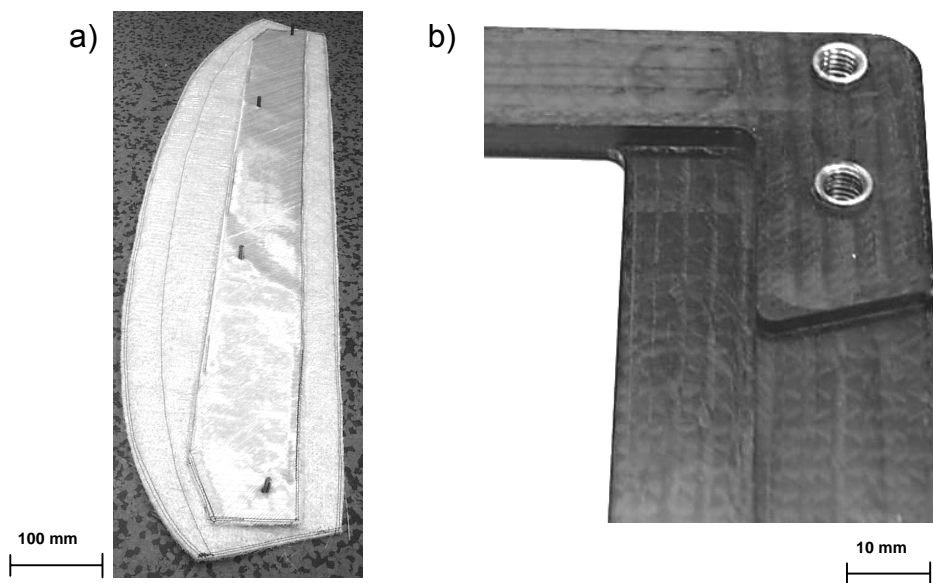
a) Spoilerlippenpreform für die Automobilindustrie, b) Nähmaschinen-Spannrahmen (Bauteil)
